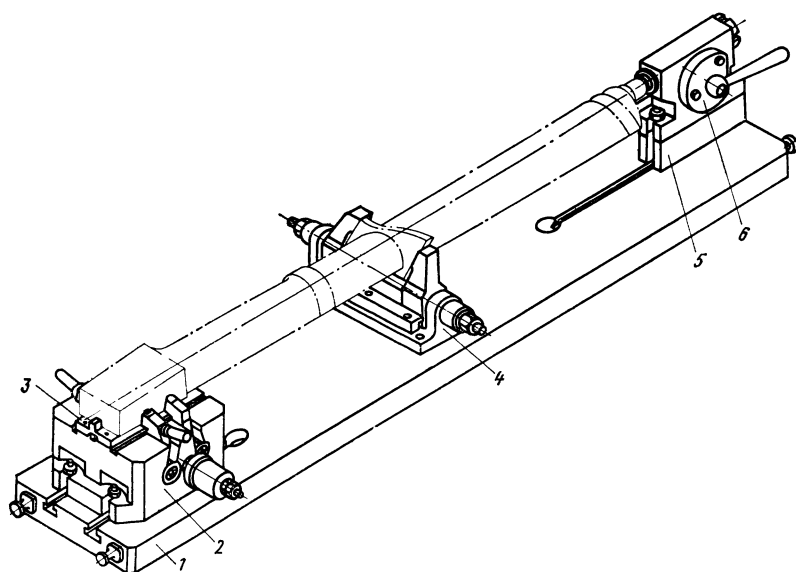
Агрегатированное станочное приспособление для рабочих лопаток турбин
